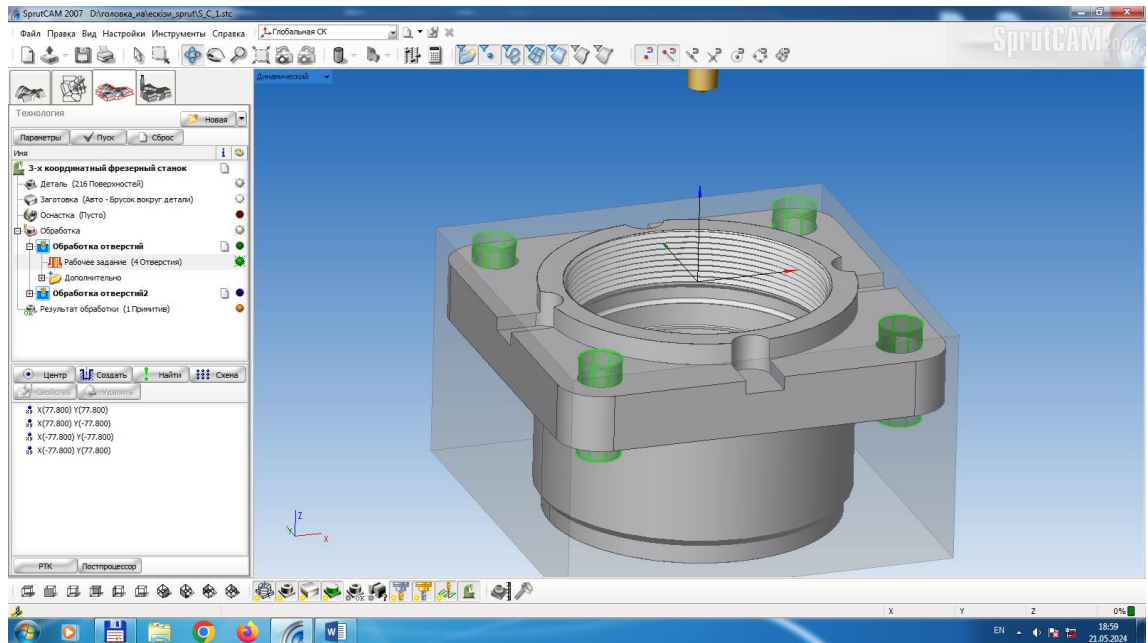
Інструмент і деталь після обробки на верстаті.
